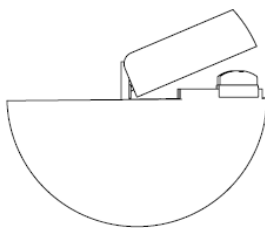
Detailní vyznačení místa pro zachytnutí krytky
